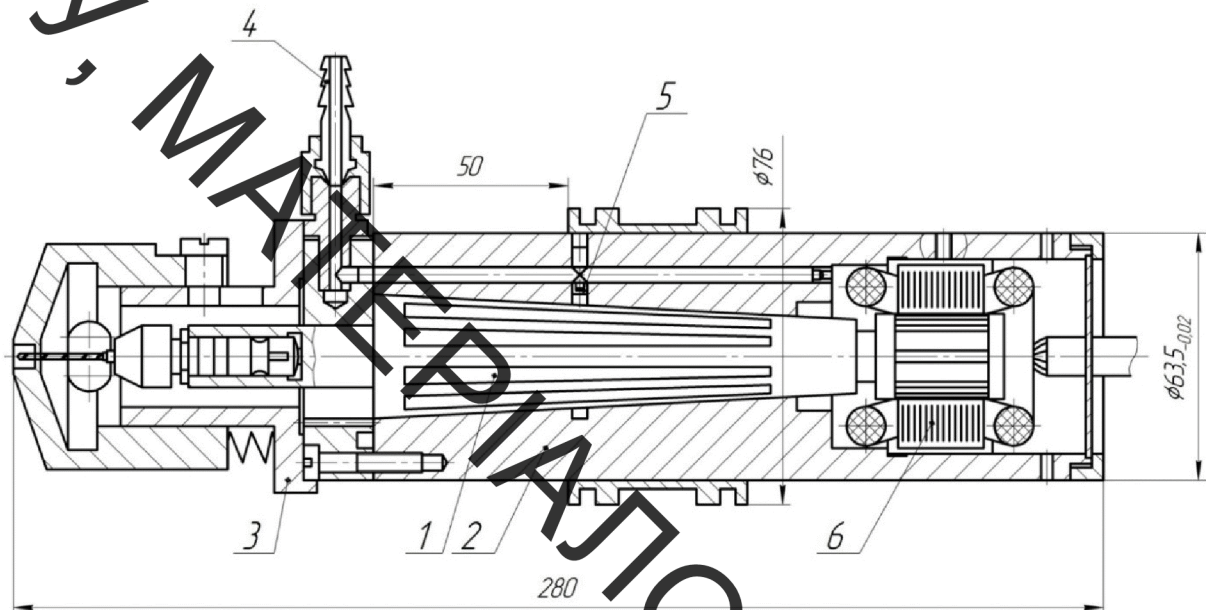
Шпиндель на пневматичній конічній опорі
